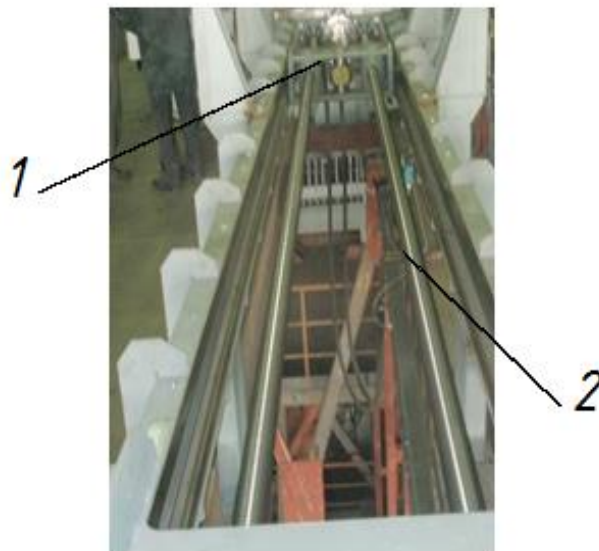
Привід подачі шихти в зону плавки: 1 – редуктор; 2 – гвинтова передача
